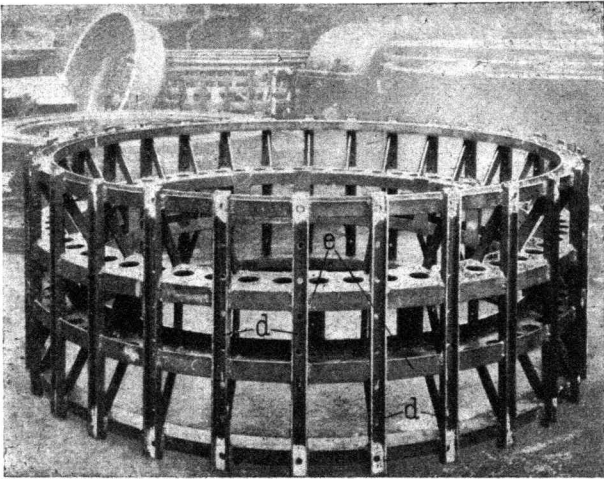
Geschweißtes Gerippe des Rotors des Triebmotors.
